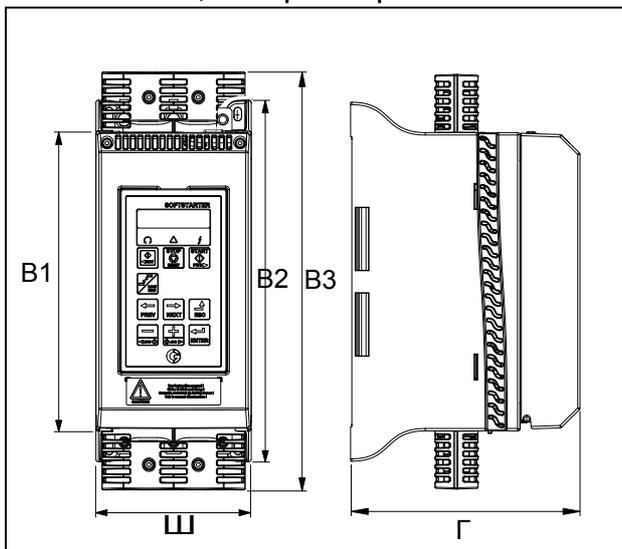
Габаритные размеры Emotron TSA типоразмеров 1 и 2.
